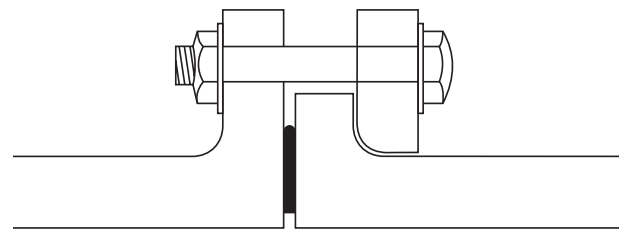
Prinzip einer Flanschverbindung
